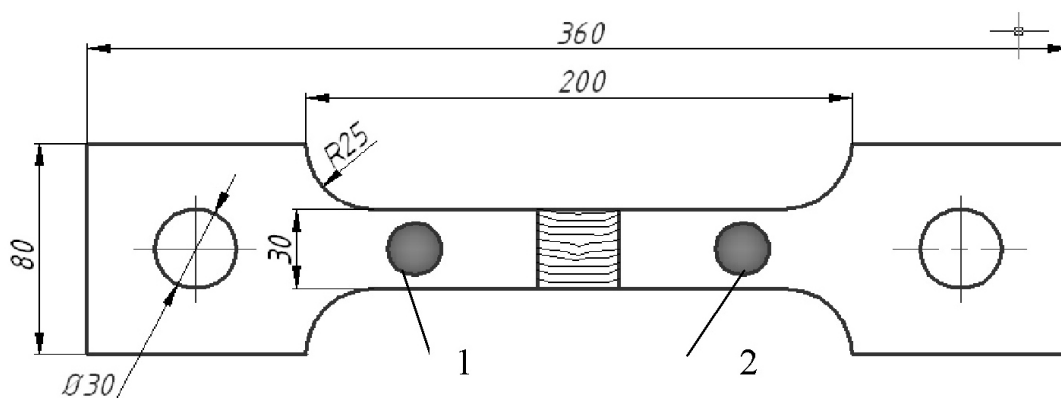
Образец для испытаний и расположение пьезопреобразователей (1, 2)
